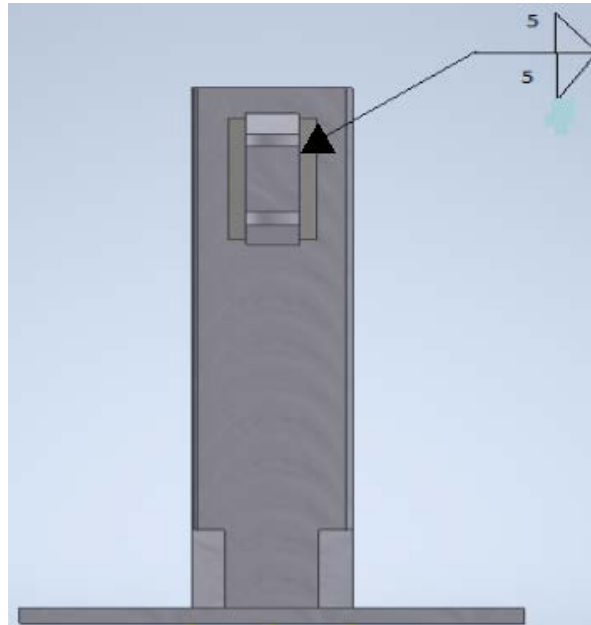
Identificación del cordón de soldadura entre la columna de sección cuadrada y el brazo de soporte del horno.
